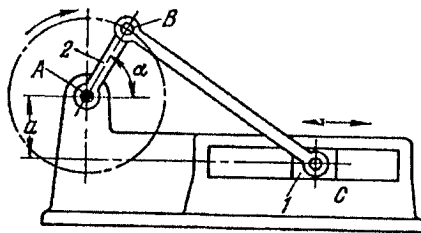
Кривошипно-повзунний дезаксіальний механізм:
